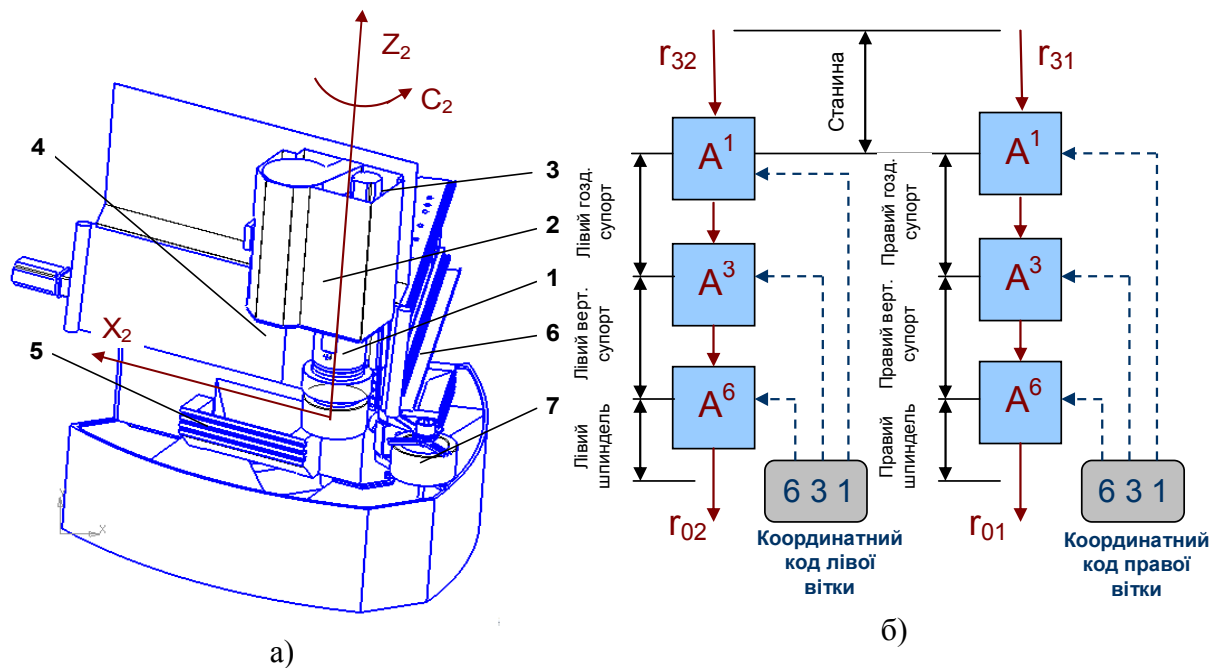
Основні вузли (а) та формоутворююча структура (б) двошпindelного вертикального токарного верстата з ЧПК мод. ПАБ-350 : 1 – шпindelі; 2 – шпindelні бабки; 3 – вертикальні супорти; 4 – горизонтальні супорти; 5 – інструментальні системи; 6 – станина; 7 – перевантажувач
